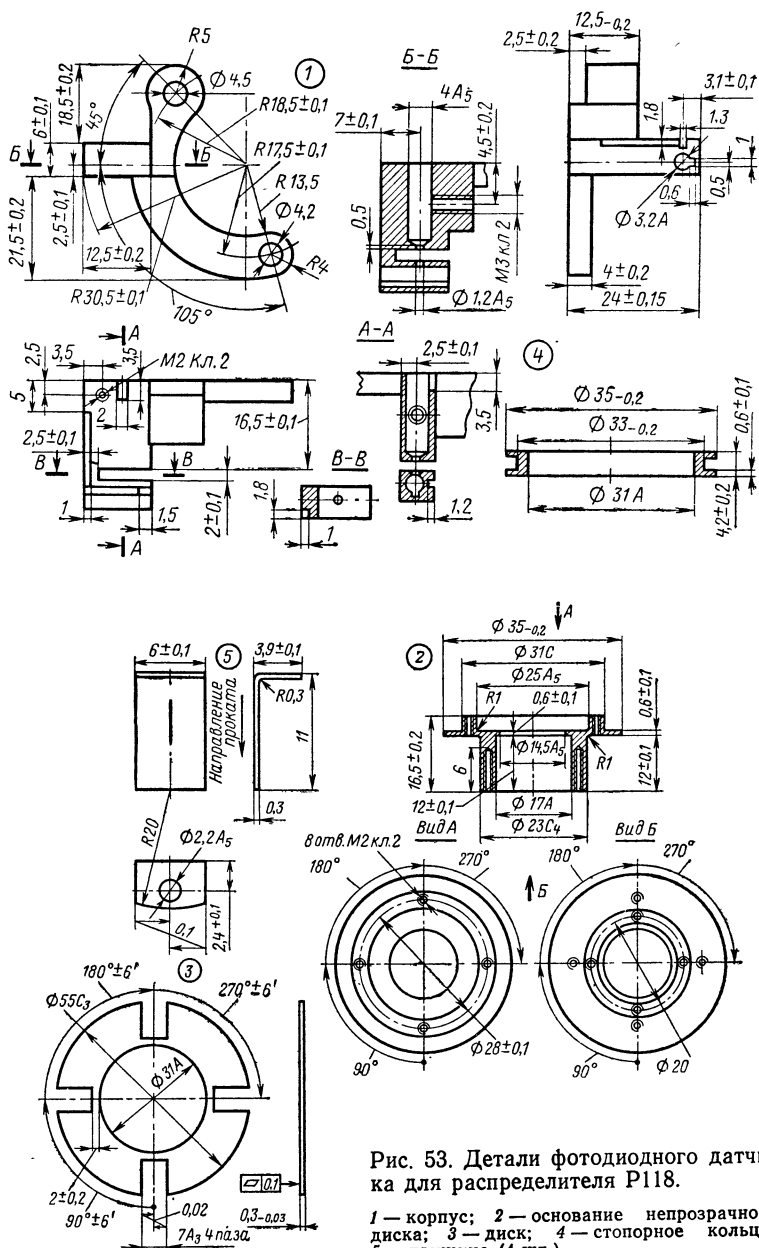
Детали фотодиодного датчика для распределителя Р118.
